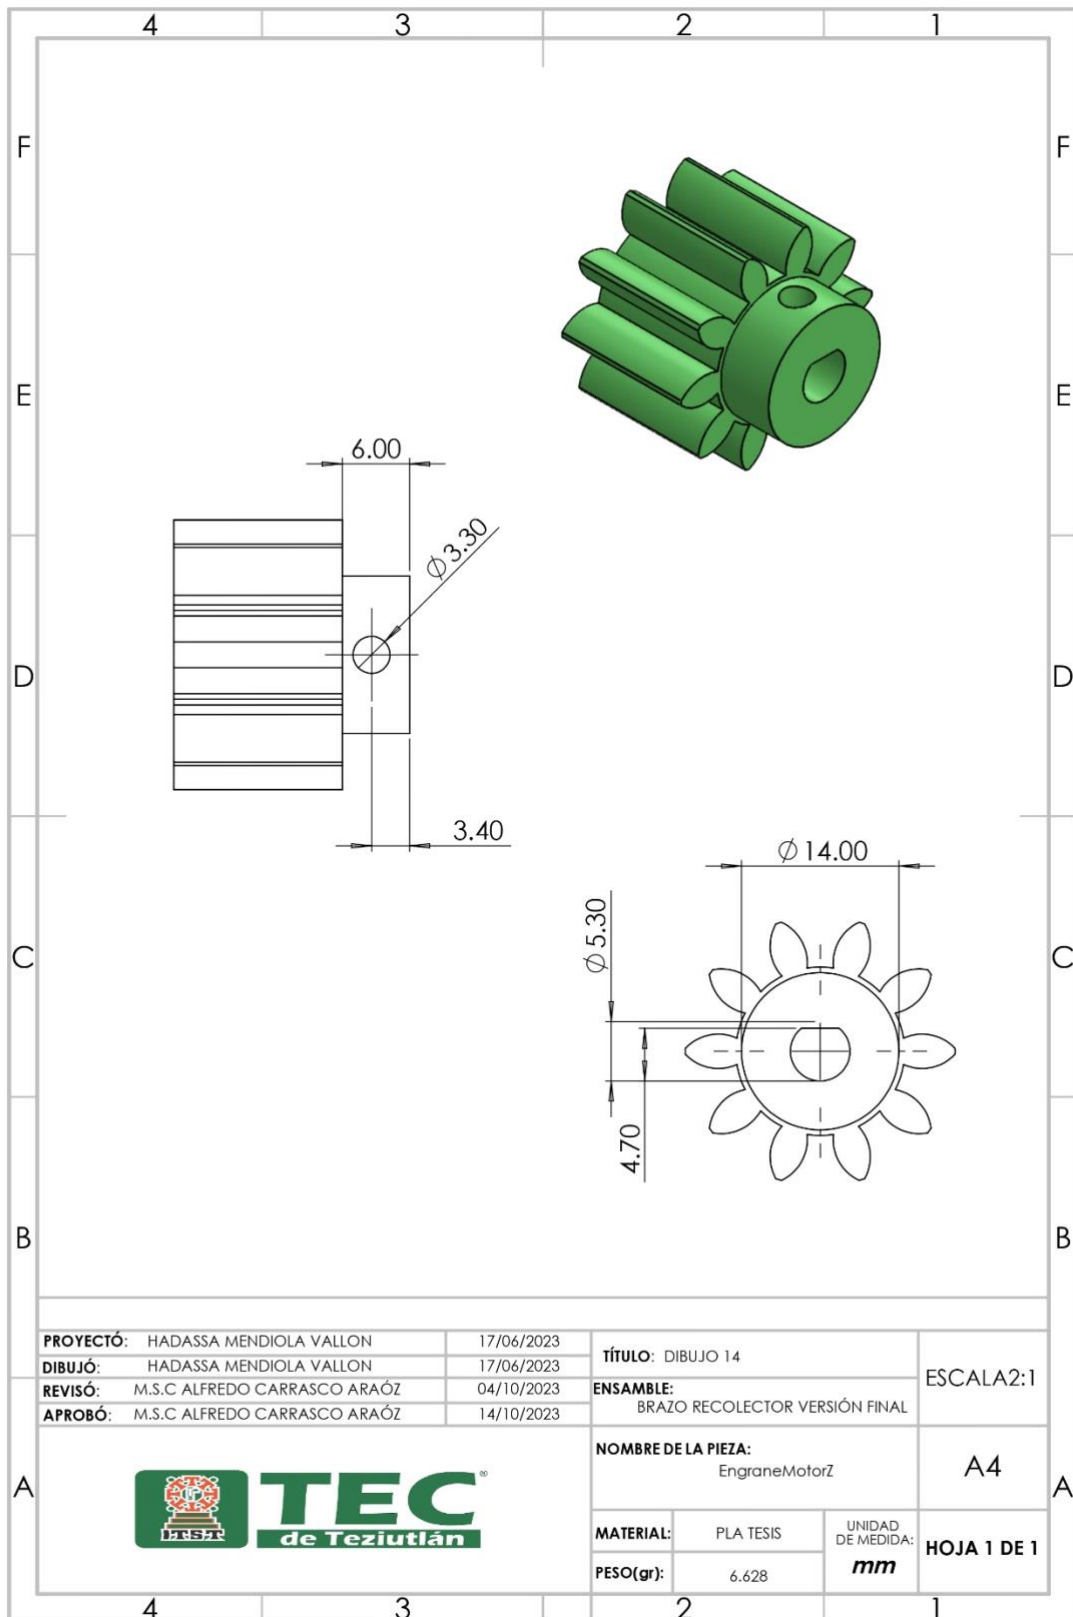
Dibujo en SolidWorks "Engrane Motor Z". Autor propio
